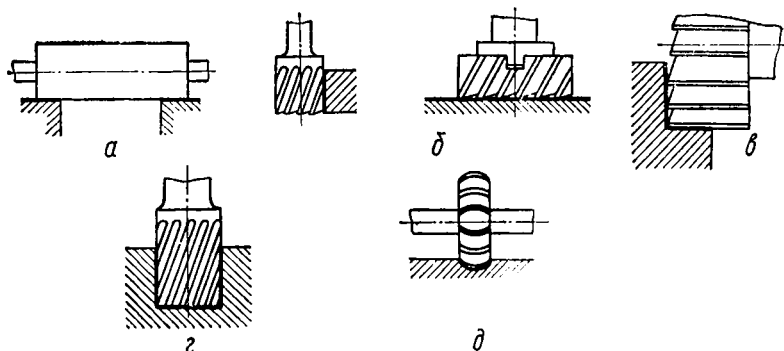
Основные схемы обработки плоскостей фрезерованием
